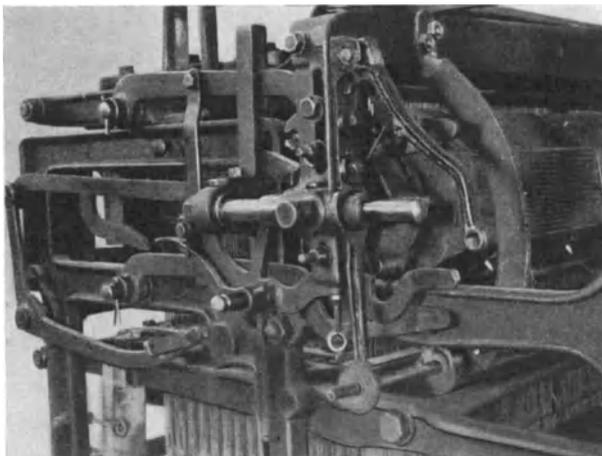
Ansicht einer Prismenschaltvorrichtung mit Hakensteuerung.
